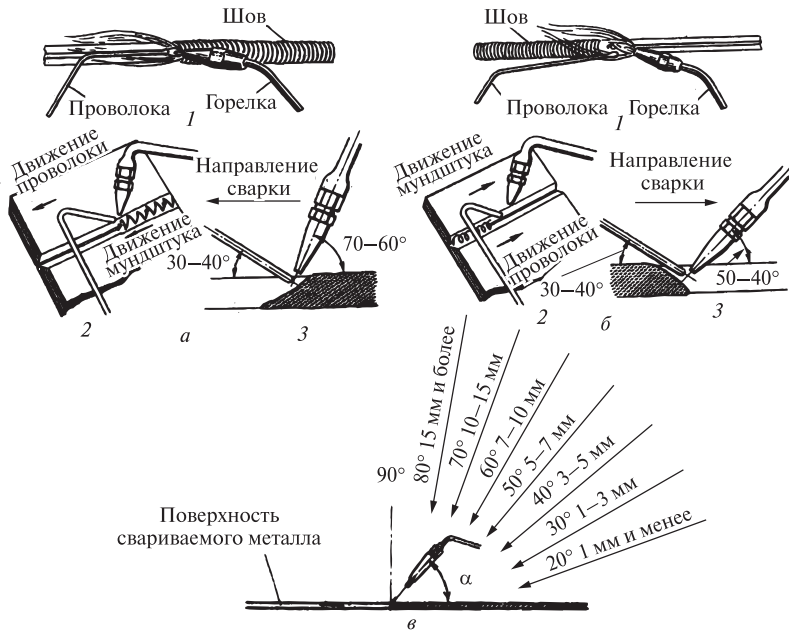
Способы сварки и угол наклона мундштука горелки: а – левая; б – правая; в – угол наклона мундштука при разных толщинах металла; 1 – момент сварки, 2 – схемы движений мундштука и проволоки; 3 – углы наклона мундштука и проволоки
